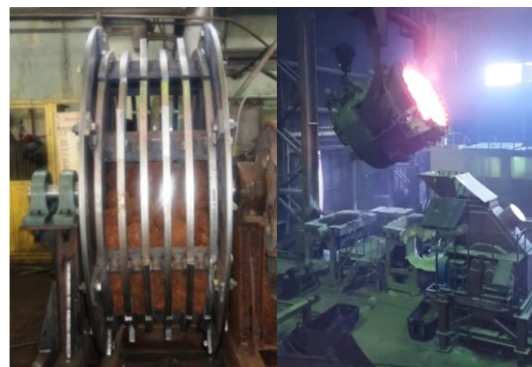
Конструкция ротора для верхней подачи расплава и подача расплава в опытную установку роторного типа
